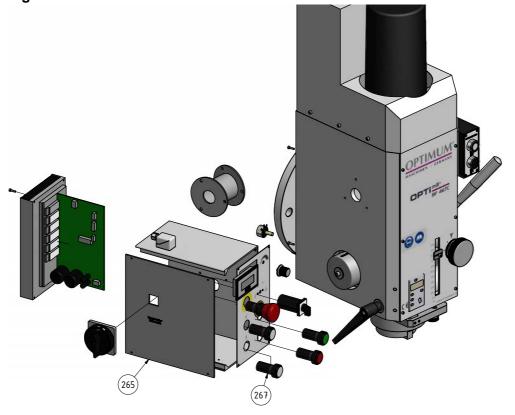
Fräskopf - Milling head BF46 TC Vario
